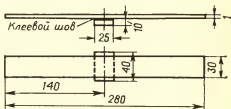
Стандартный образец для испытания прочности при неравномерном отрыве.
